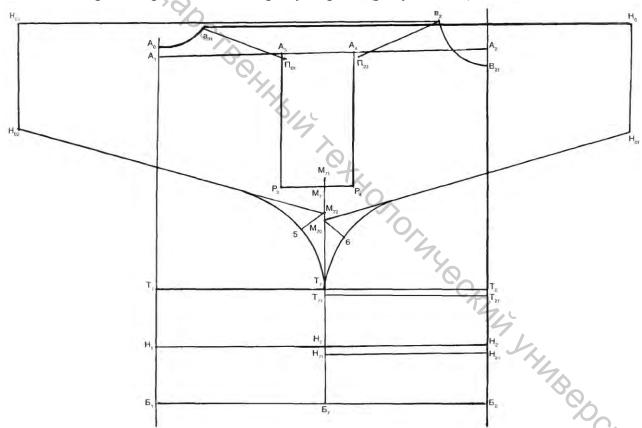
Чертеж конструкции изделия с цельнокроеными рукавами
